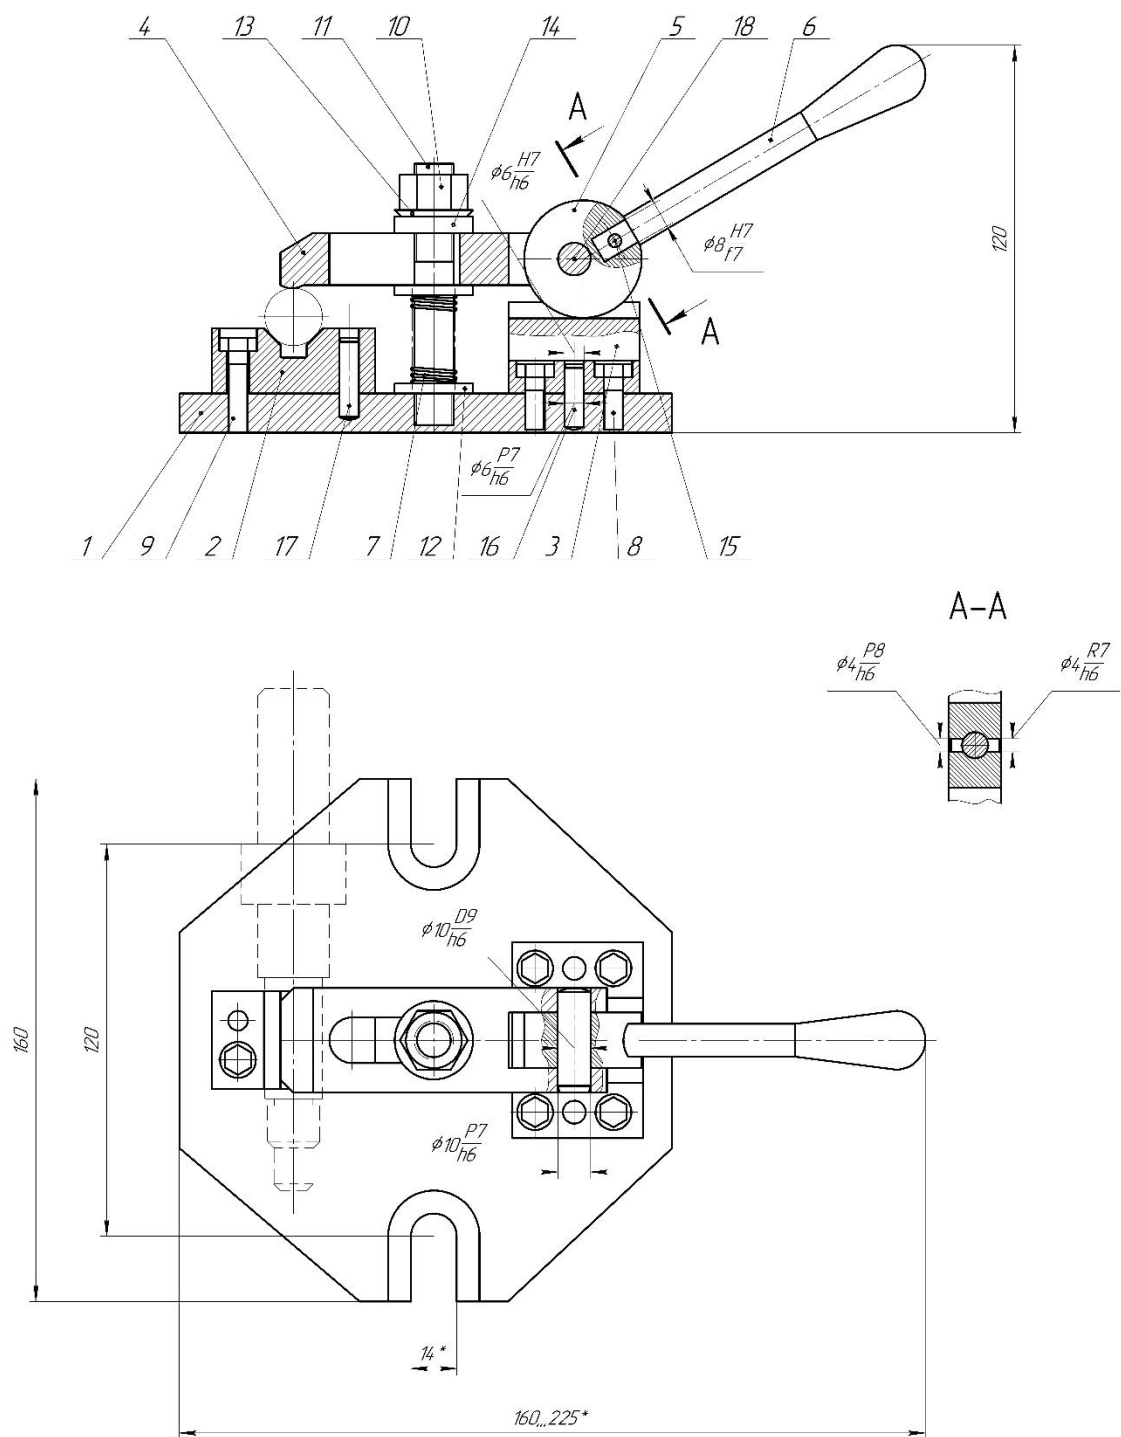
Пристрій для затискання валика насоса: 1 – плита; 2 – призма; 3 – опора; 4 – притискач; 5 – ексцентрик; 6 – рукоятка; 7 –
